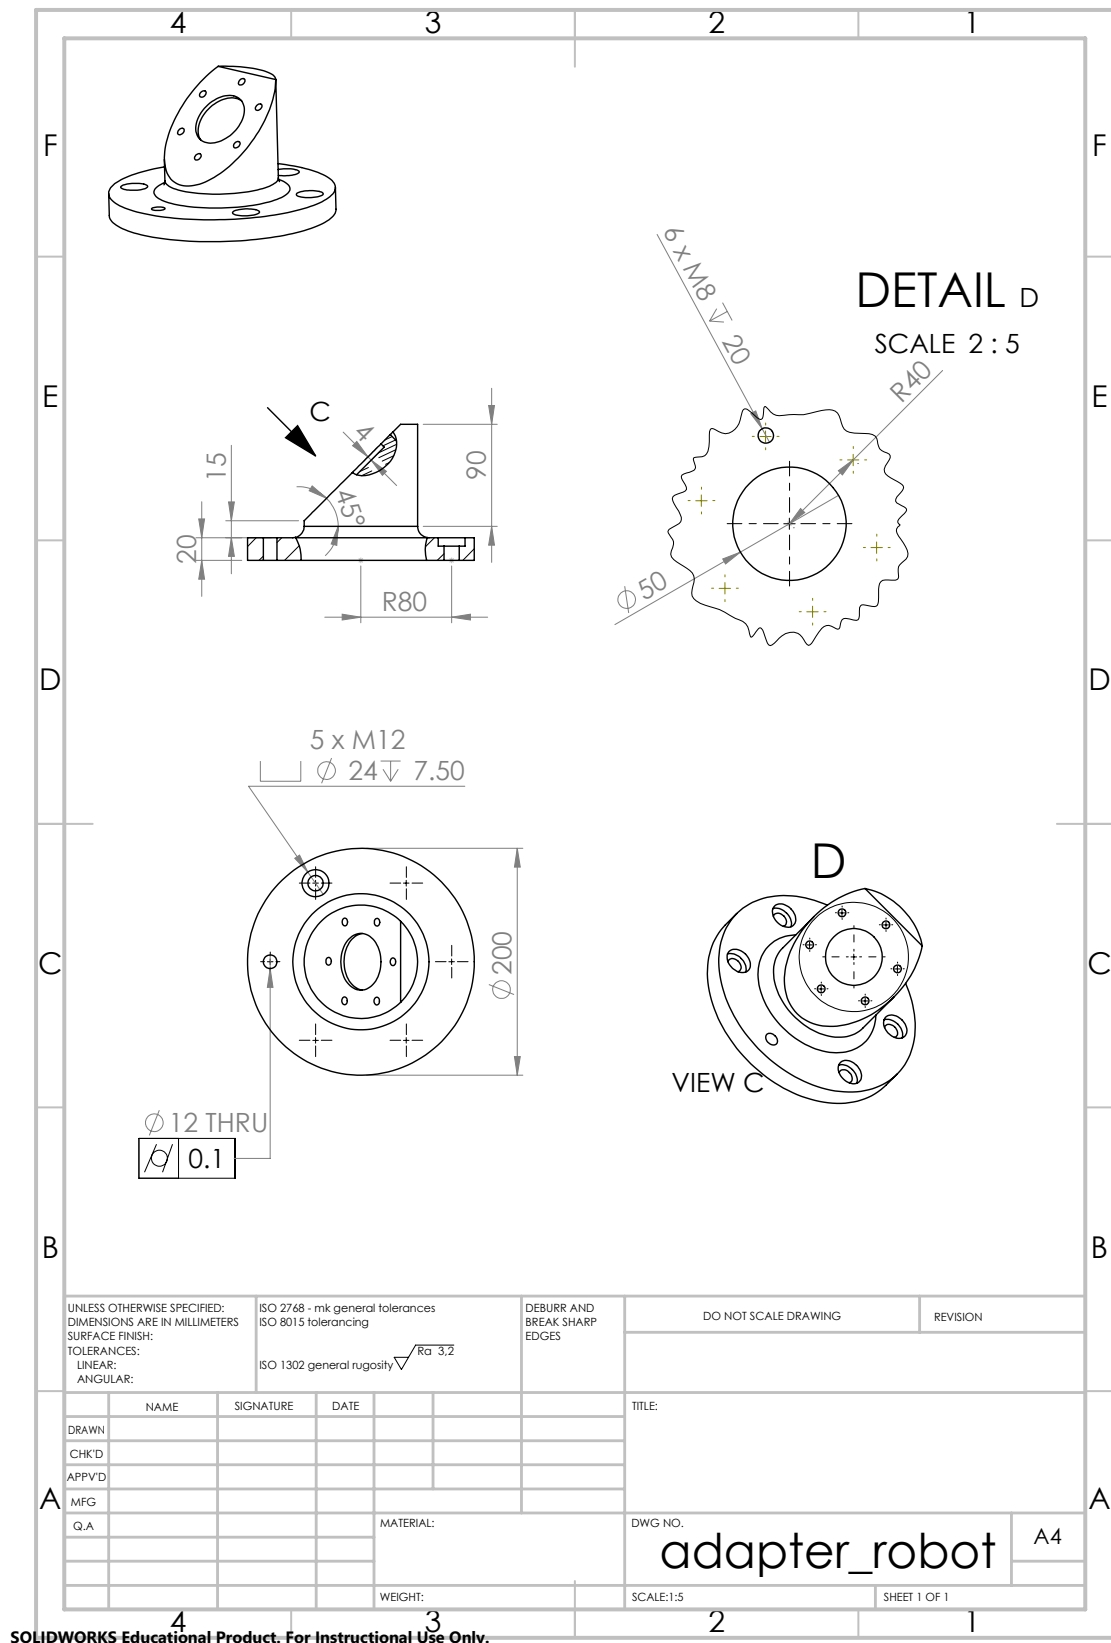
Desenho Técnico: Adaptador Braço-AFC
